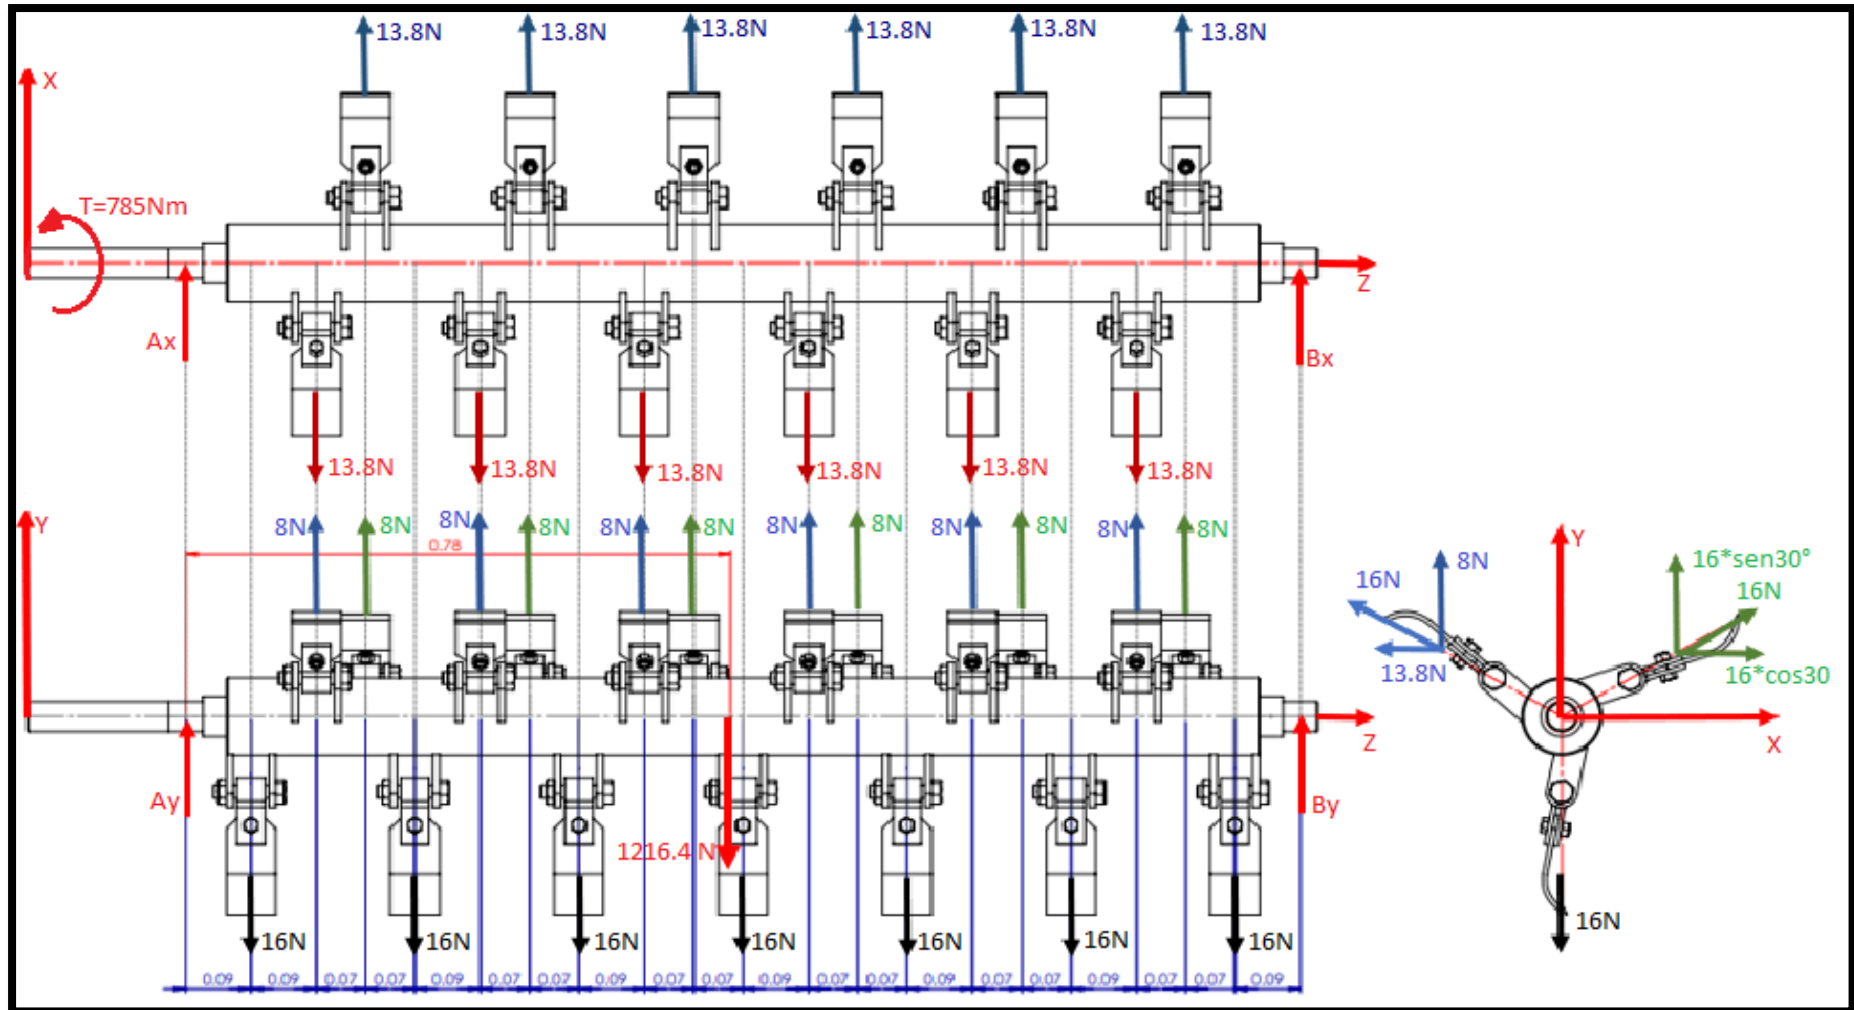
Diagrama de cuerpo libre corresponde al sistema de corte, donde se muestra una vista de planta completa del conjunto de cuchillas instaladas en el eje, todos en relación con las cargas aplicadas en cada punto de apoyo
